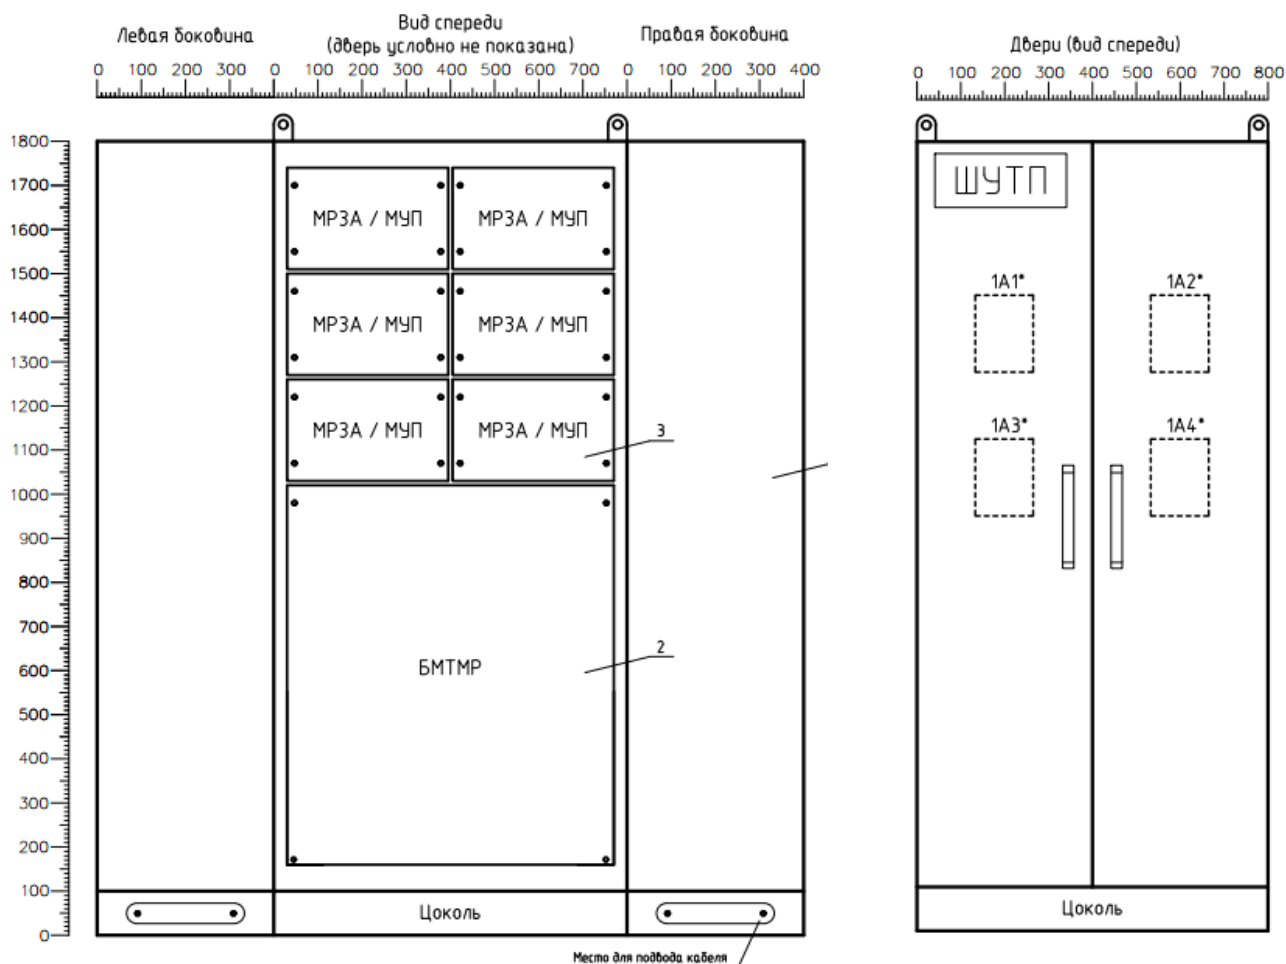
Общий вид и габаритные размеры ШУТП.
